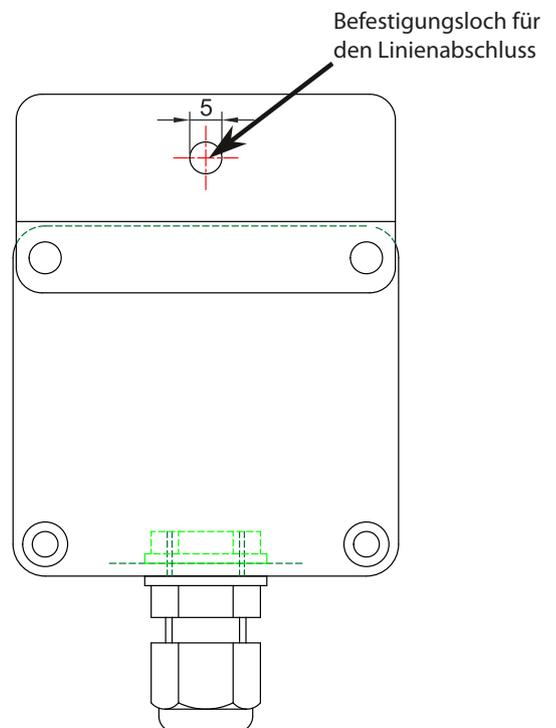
Befestigungsmaße für die Montage des ProReact EN Analogue End-of-line Unit
